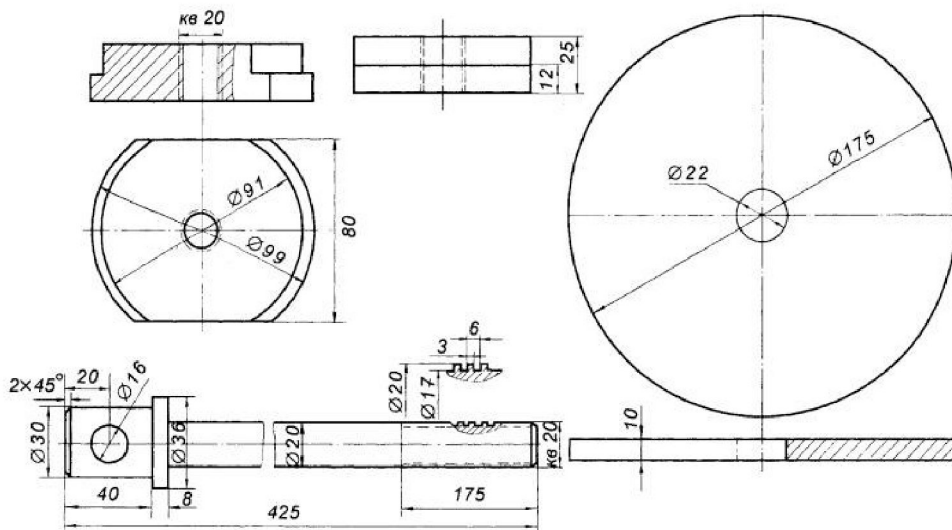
Съемник для выпрессовки гильз из блока цилиндров.
